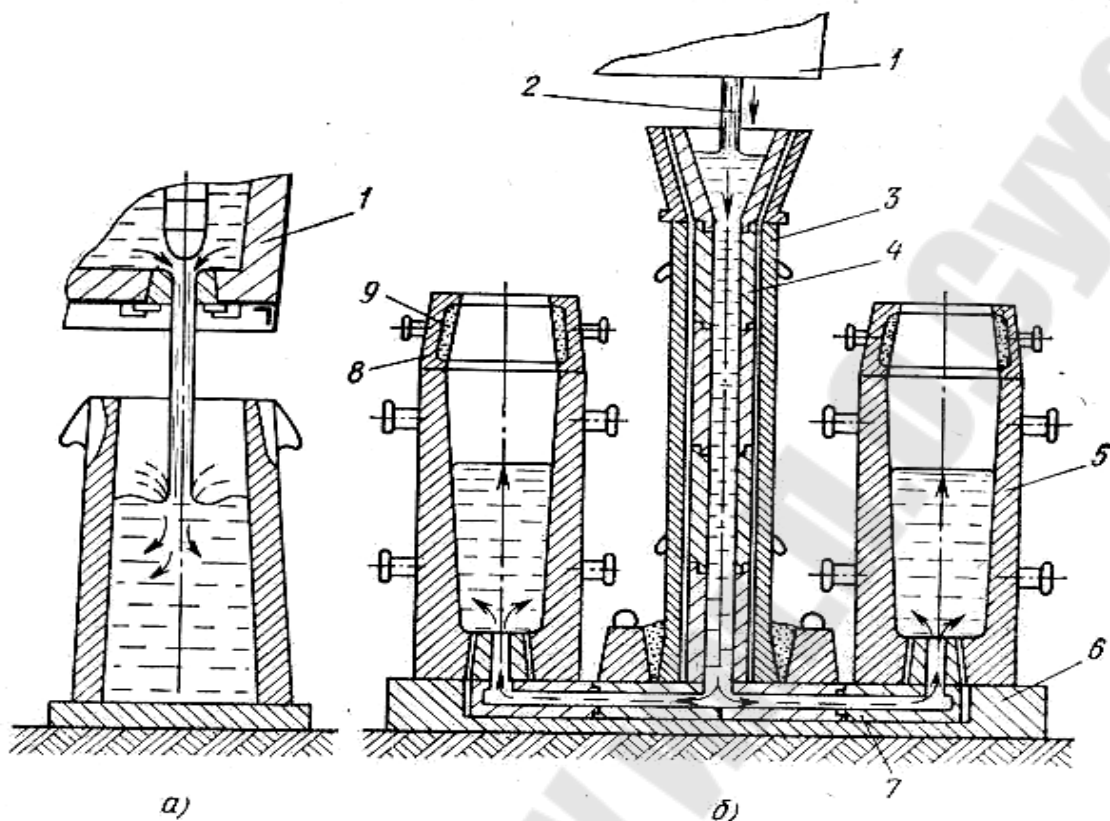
Схемы разливки стали: *а* – сверху; *б* – снизу (сифоном)
